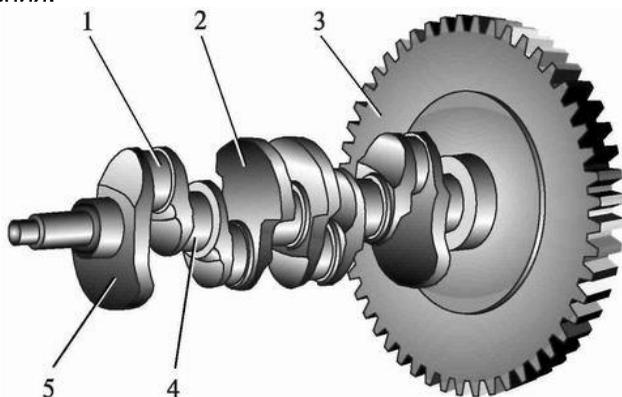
Коленчатый вал двигателя с маховиком: 1 – шатунная шейка; 2 – противовес; 3 – маховик с зубчатым венцом; 4 – коренная (опорная) шейка; 5 – коленчатый вал двигателя
